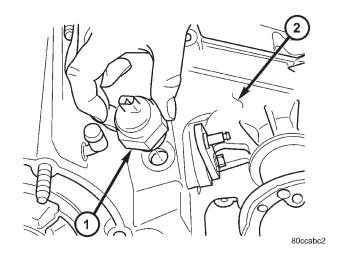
Desmontaje del sensor de posición de la caja de cambios
